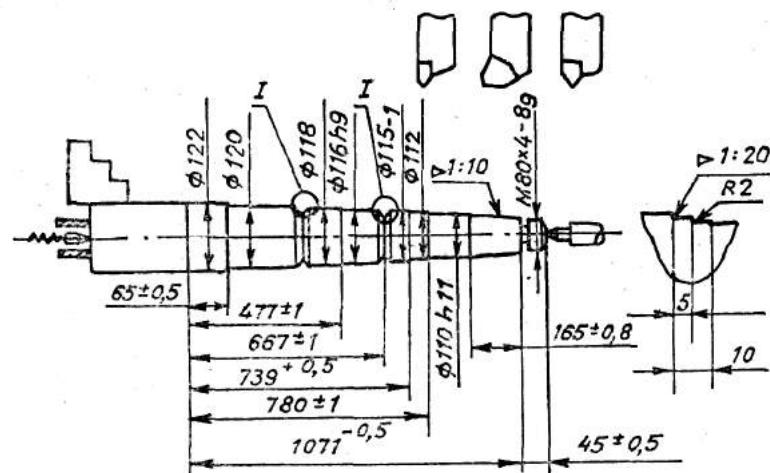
Багатопозиційний РТК для обробки валів мод. АСВР-01:
